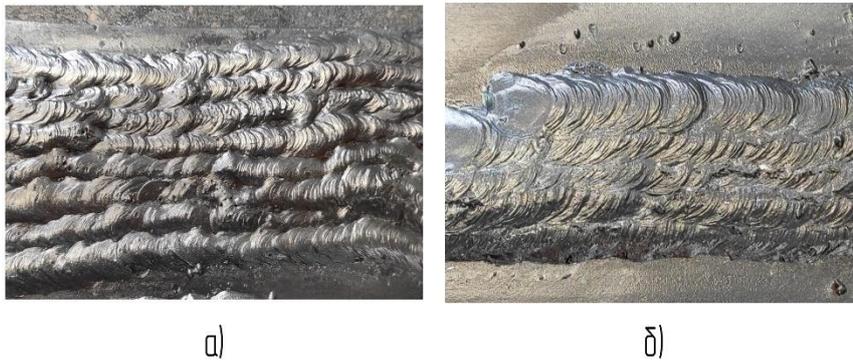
Профиль наплавленной поверхности: а) – сплавление валиков плохое; б) – сплавление валиков хорошее (перекрытие 50%).
